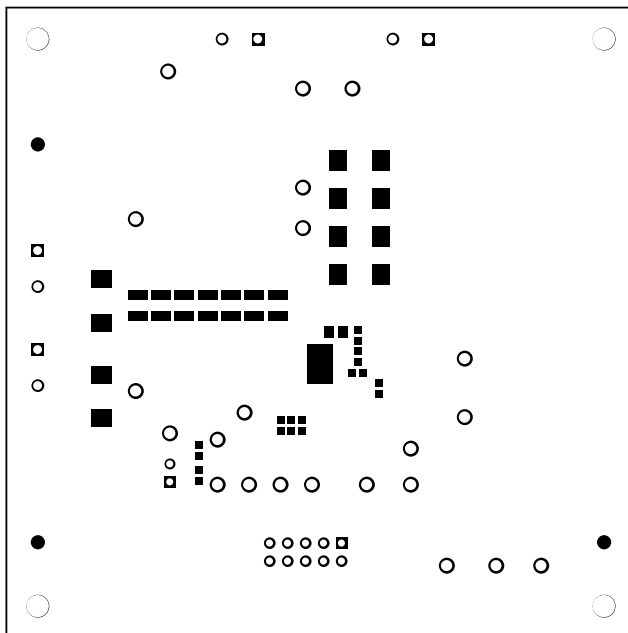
PWR-784EVM 底部阻焊层 (顶视图)
